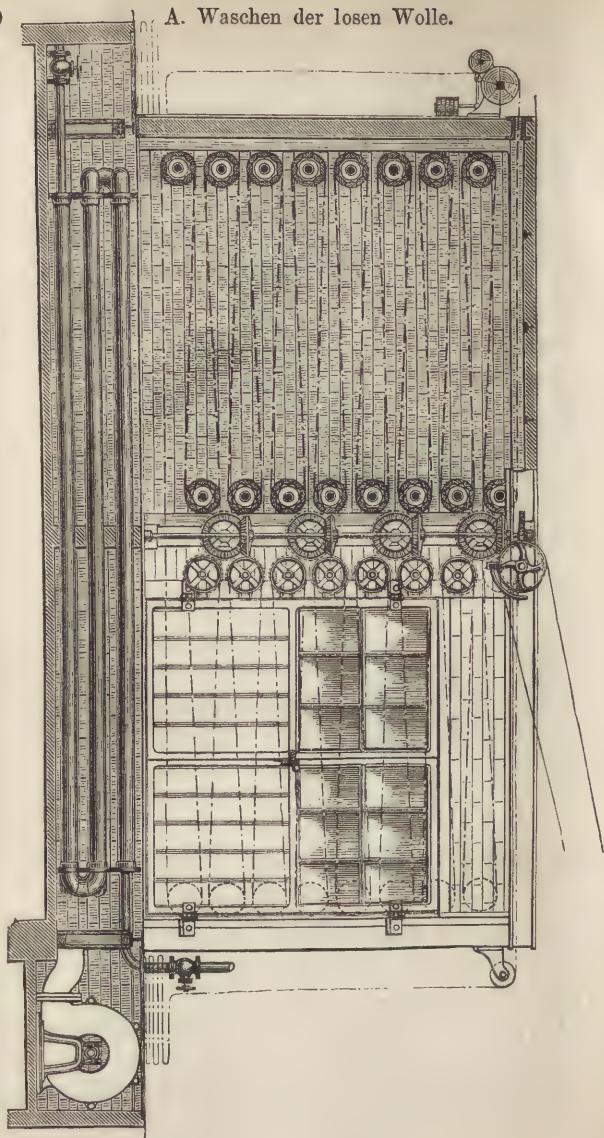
Carbonisirmaschine für wollene Gewebe.
